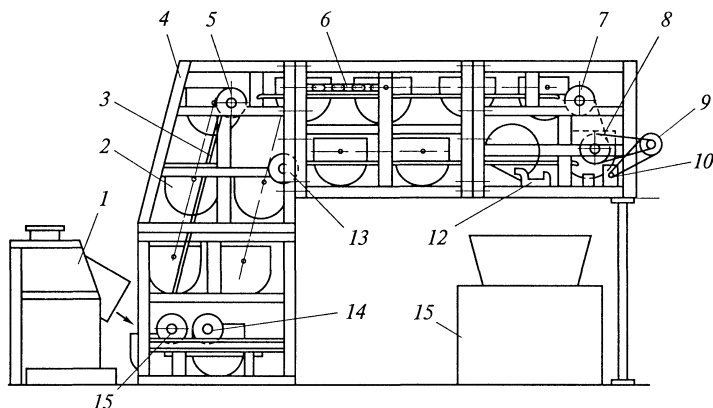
Агрегат цепного типа с однофазной схемой приготовления теста
